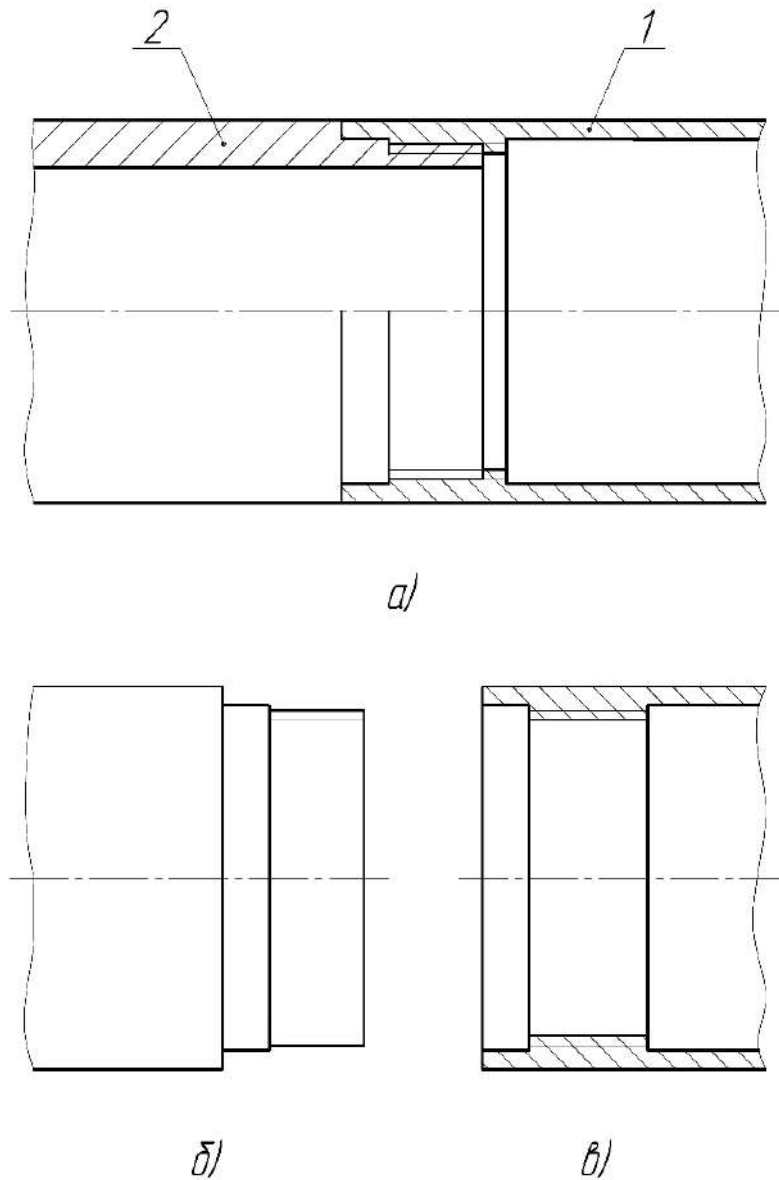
Резьбовое соединение: а – сборка, б – труба с наружной резьбой, в - труба с внутренней резьбой
